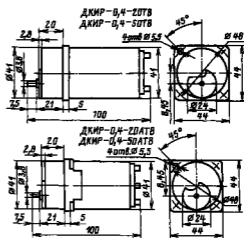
Габаритные и установочные размеры двигателей ДКИР-ТВ, ДКИР-АТВ
